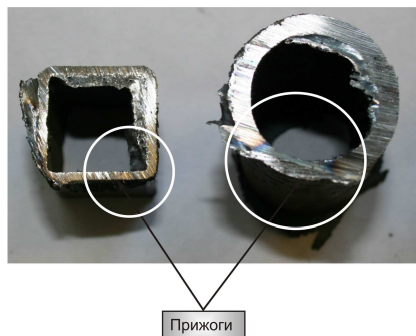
Внешний вид заготовок с дефектами в виде прижогов
